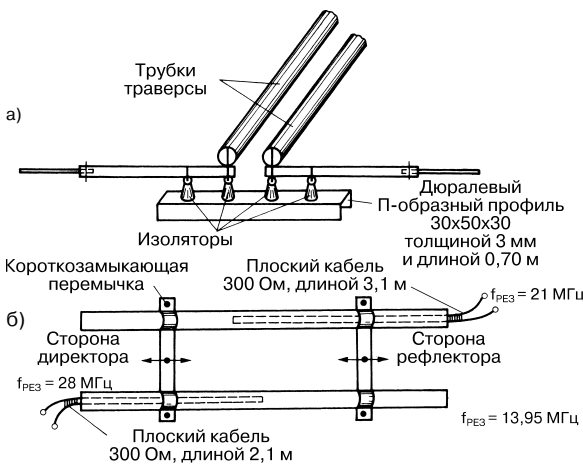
Устройство и настройка пассивных элементов: а – конструкции директора и рефлектора; б – траверсы с настроенными шлейфами
